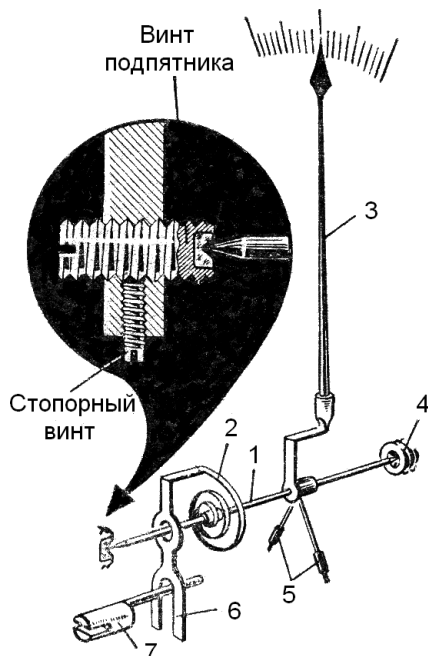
Устройство подвижной части измерительных механизмов: 1 — ось; 2 — спиральная пружина; 3 — указательная стрелка; 4 — подпятник; 5 — противовес; 6 — вилка корректора; 7 — винт корректора
